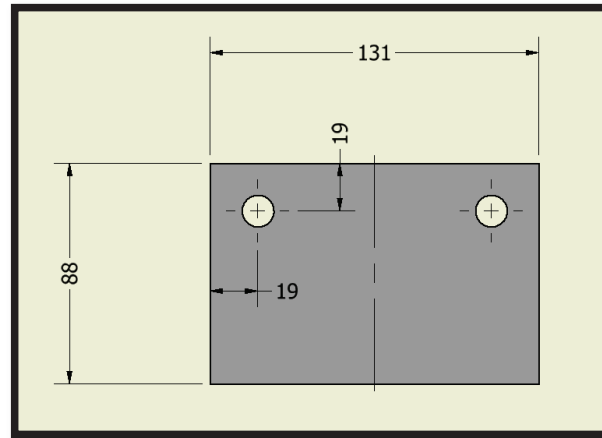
Dimensiones para la placa de conexión columna-soporte contrapeso.
